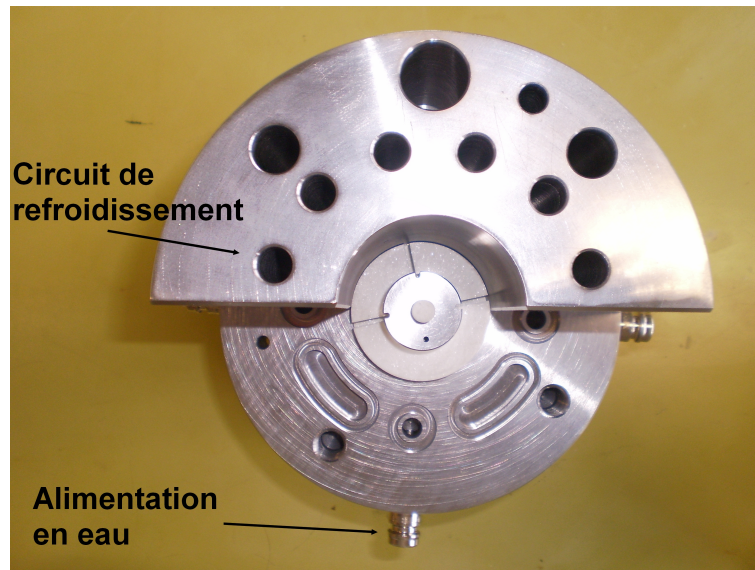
Vue de dessus du moule PvT thermoplastique
